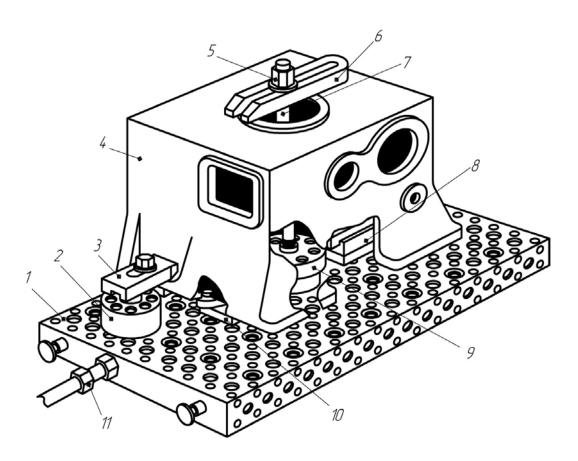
Конструкция универсально—сборного переналаживаемого приспособления для установки корпусной детали: 1 — гидроплита; 2, 9 — гидроцилиндры; 3, 6 — прихваты; 4 — заготовка; 5 — гайка; 7 — шпилька; 8, 10 — опоры; 11 — штуцер
